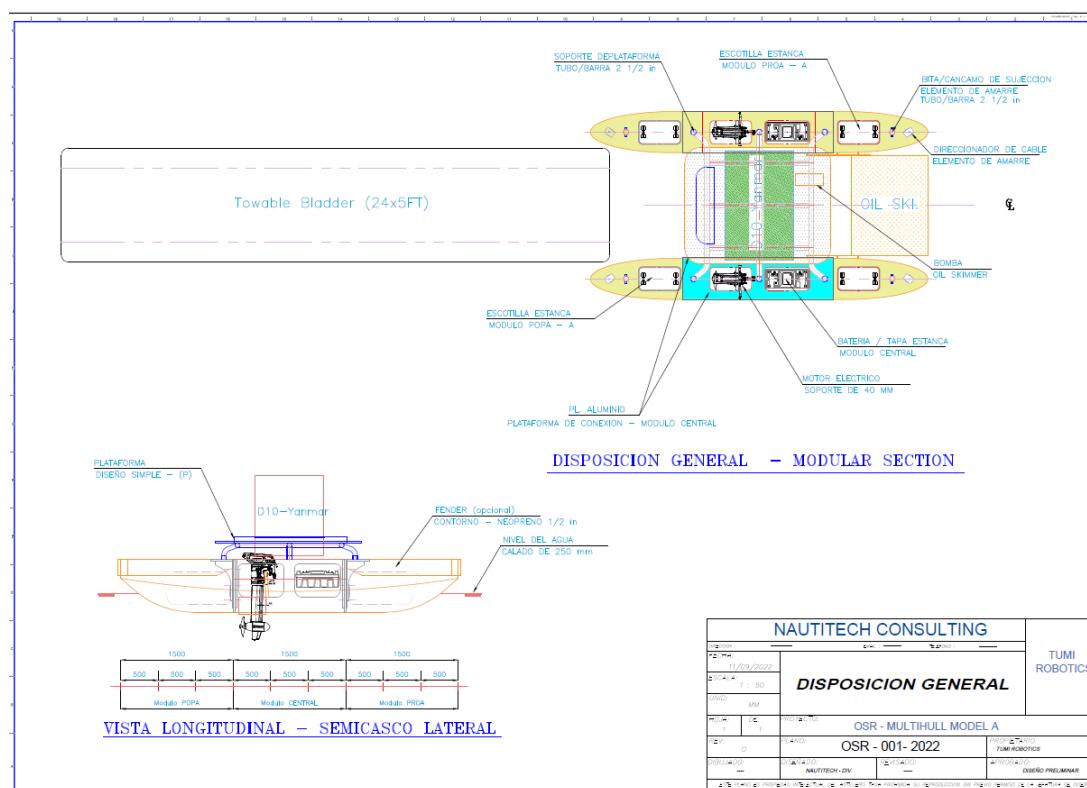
Plano preliminar - Disposición General. (Elaboración propia)
